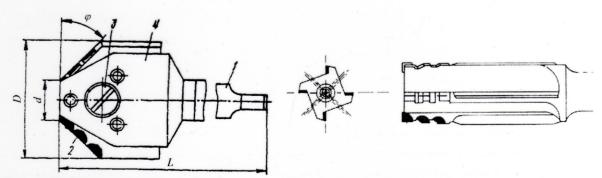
Сверла, оснащенные ПСТМ, с механическим креплением режущих элементов (a); с прямыми (b) и спиральными (b) канавками и паяными режущими элементами: 1 – корпус; 2, 3 – сменные ножи (устанавливают в сверла и крепят винтами 4 к корпусу через фасонные отверстия).
